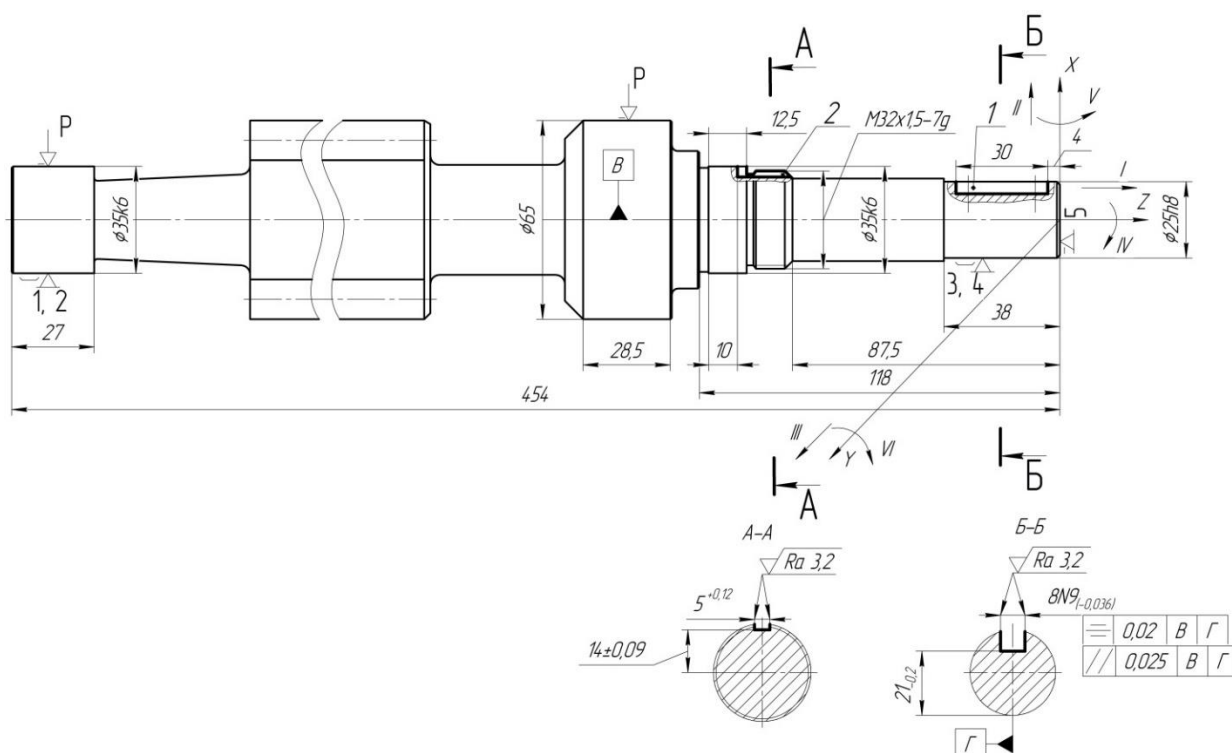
Схема базування заготовки на операцію 030 Комплексна з ЧПК (варіант 2)
